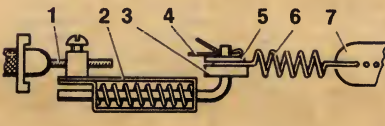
Крепление троса к рычагу дроссельной заслонки: 1 — трос; 2 — компенсатор; 3 — рычаг дроссельной заслонки; 4 — шплинт; 5 — шайба; 6 — пружина; 7 — полоса.
